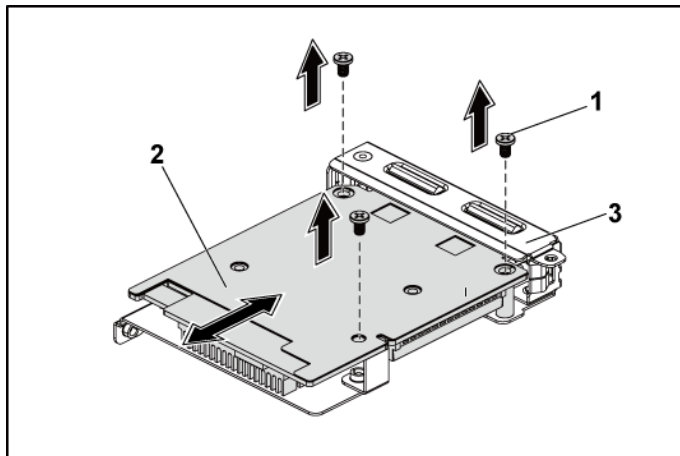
Retrait et installation de l'assemblage de la carte mezzanine 10GbE
